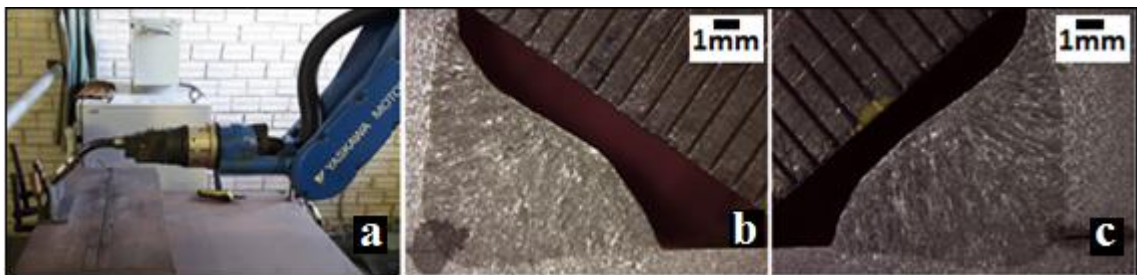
(a) Preparação para soldagem teste na posição horizontal de soldagem. (b) e (c) Macrografias para deposição na posição horizontal de soldagem. Ataque Nital 10%.
